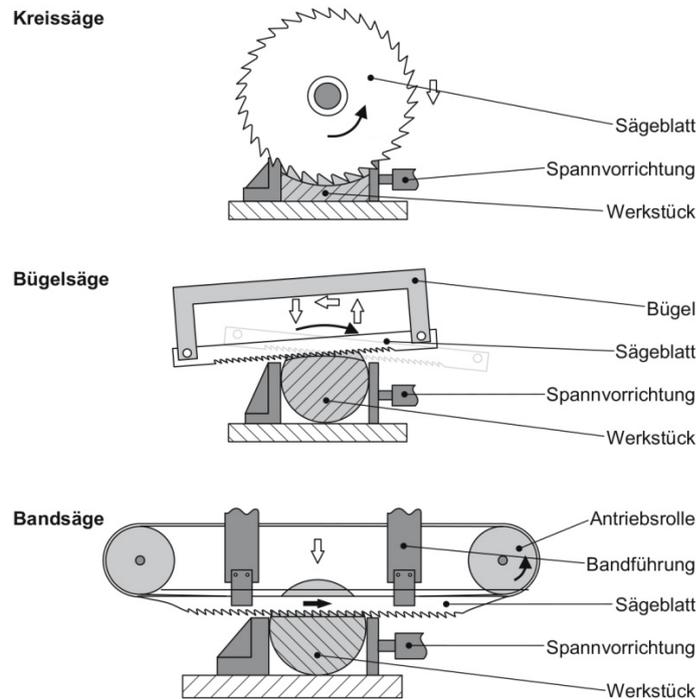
Sägemaschinen; Quelle: Werkzeugmaschinen - Maschinenarten und Anwendungsbereiche, Springer
